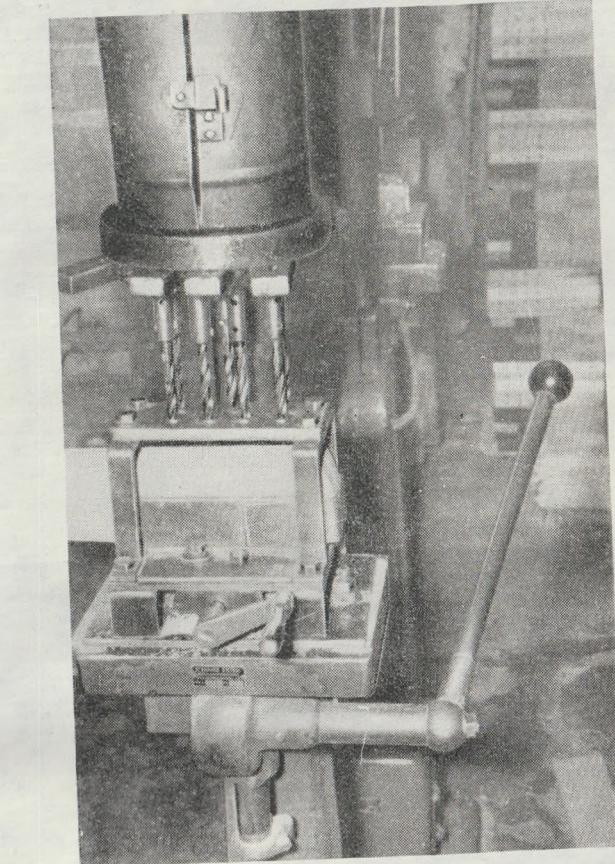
Сверление отверстий в головках для крепления колковой механики на многошпиндельном сверлильном станке
